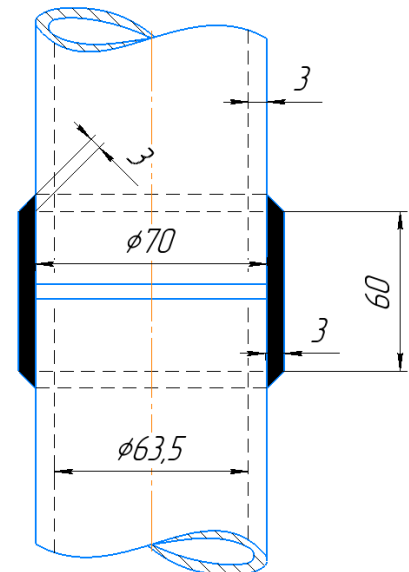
Схема зварного зразка з муфтовим з'єднанням для випробування труб
